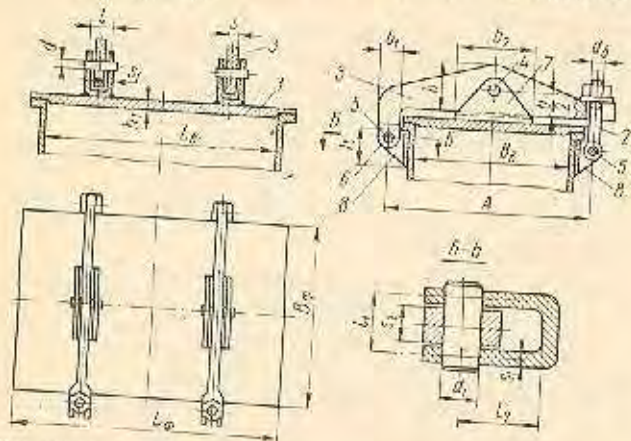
Конструкция плоской прямоугольной крышки с двумя бигельными устройствами:
